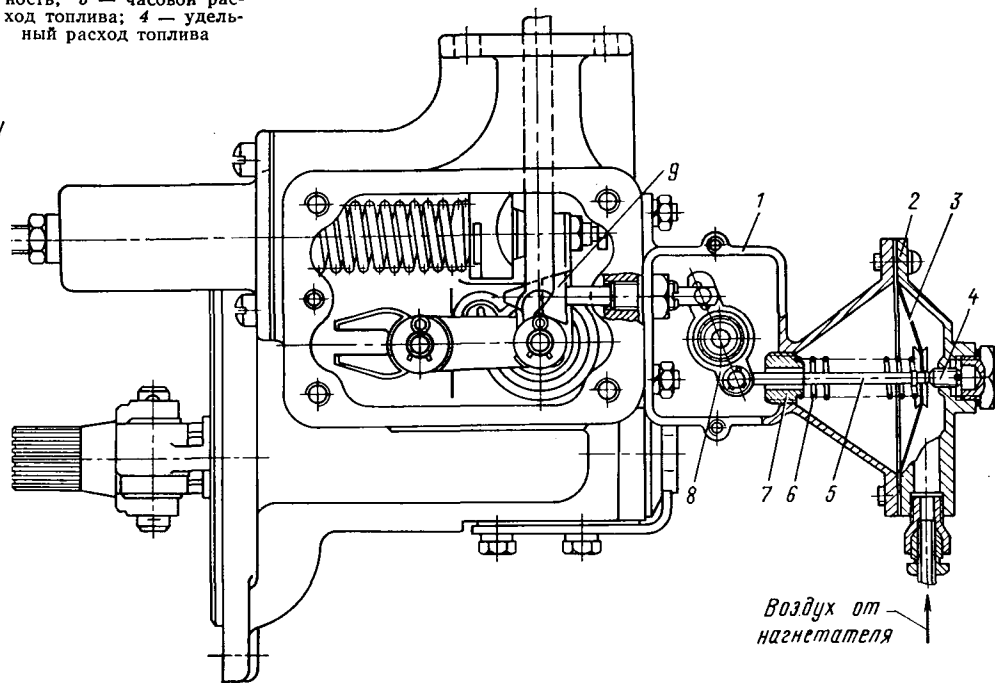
Пневматический корректор максимальной подачи топлива: 1 — корпус; 2 — крышка; 3 — диафрагма; 4 — винт установочный; 5 — тяга диафрагмы; 6 — пружина; 7 — втулка регулировочная; 8 — рычаг корректора; 9 — упорный конус
